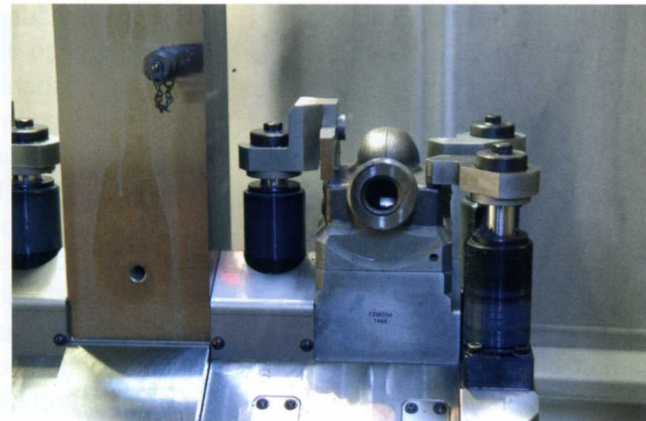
Hydraulisch betätigte Schwenkspanner spannen die Pumpengehäuse so, dass für Werkzeuge und Greifer der benötigte Freiraum bleibt
